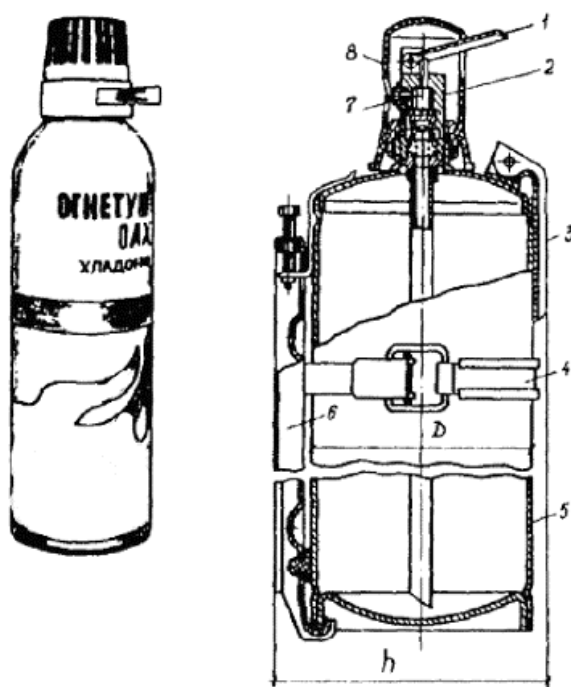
Хладоновый огнетушитель ОУБ-3А (ОУБ-7А): 1 – пусковой рычаг; 2 – запорная головка; 3 – рукоятка; 4 – крепление; 5 – баллон; 6 – кронштейн; 7 – распылительное устройство; 8 – предохранительный колпак
